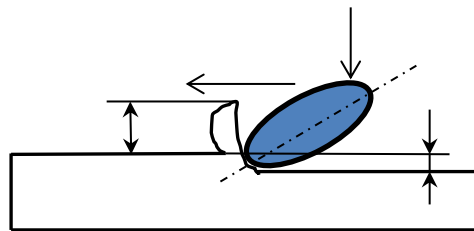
Схема втілення еліпсоїдного зерна при ВіМАО у поверхню надтвердої кераміки
